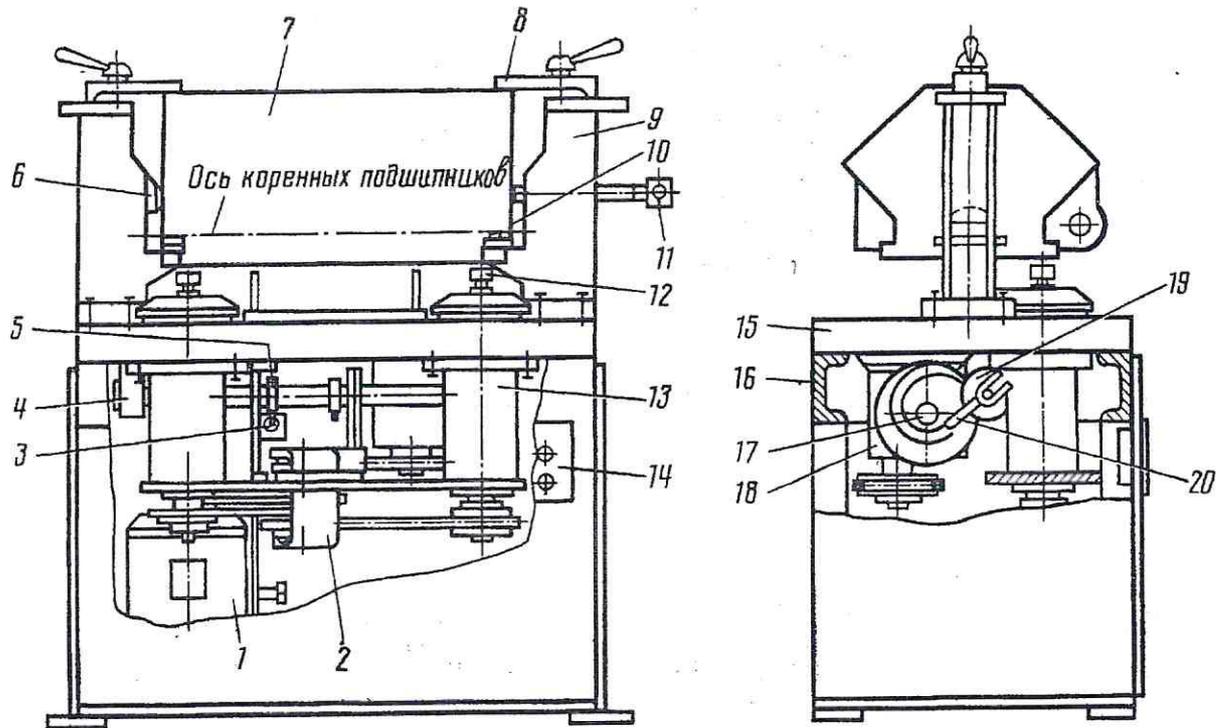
Установка для обработки базовых отверстий блока цилиндров V-образного двигателя (разработка 1-го Киевского ПО «Авторемонт» и Госавтотрансниипроекта)
